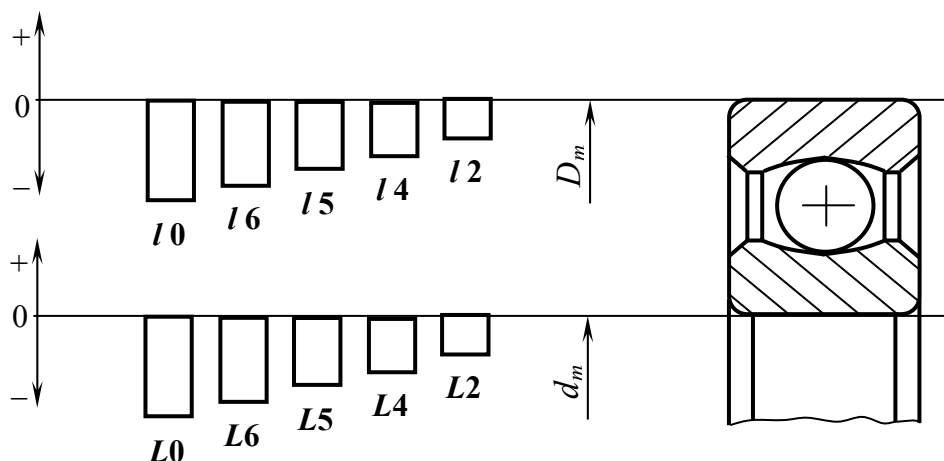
Схема расположения полей допусков средних диаметров посадочных поверхностей подшипников качения по классам точности
